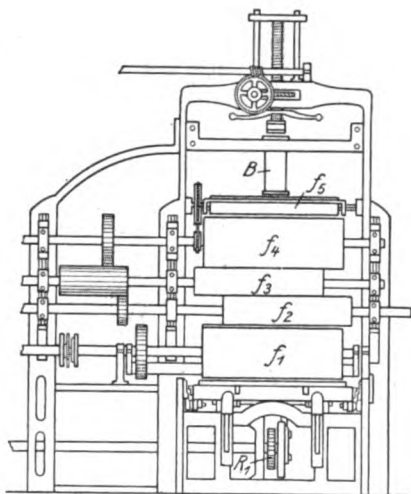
Erste Zylinderdruckmaschine, Seitenansicht
